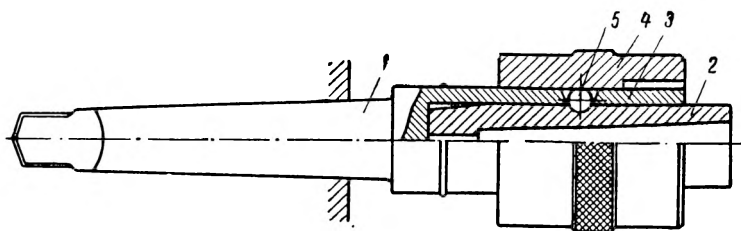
Быстросменный патрон к задней бабке токарного станка.
